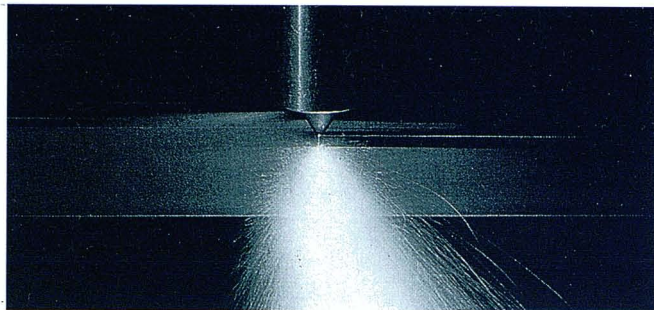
Robot industrial de soldadura mitjançant làser de CO_2
